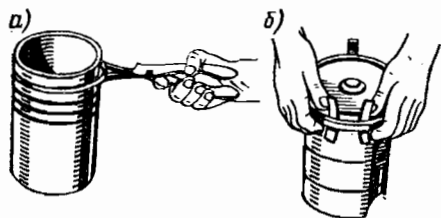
Снятие и установка поршневых колец: *а* — щипцами; *б* — с помощью металлических (медных) пластин
